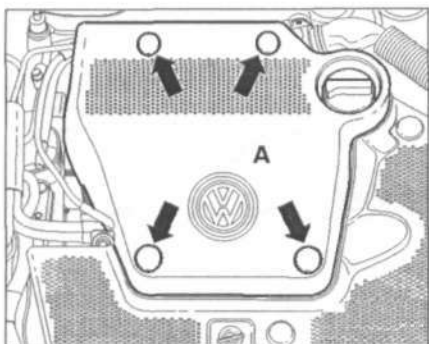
Извлеките пробки (стрелки) из крышки А двигателя с помощью отвертки.
